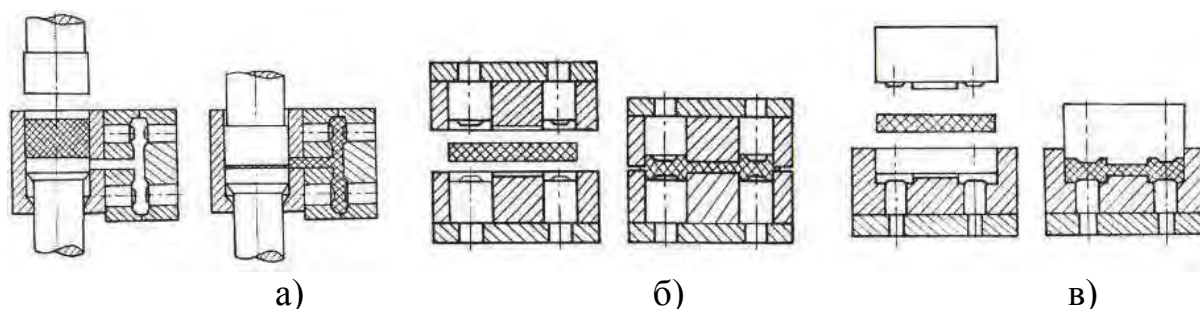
Схема получения изделий шатуна из КАМ различными методами: а – литье под давлением; б – открытая штамповка; в – закрытая штамповка
